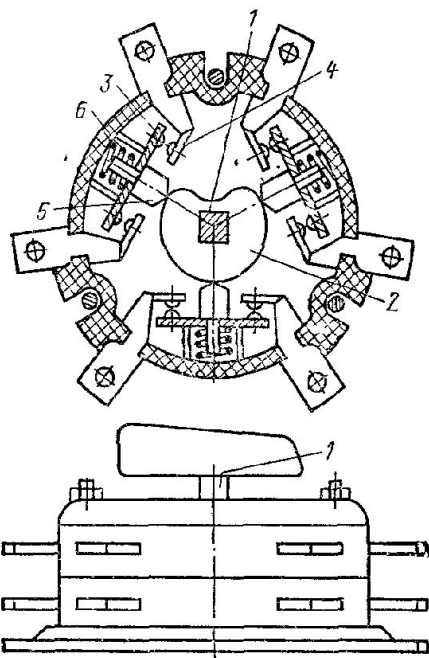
Пакетный кулачковый выключатель серии ПКВ
